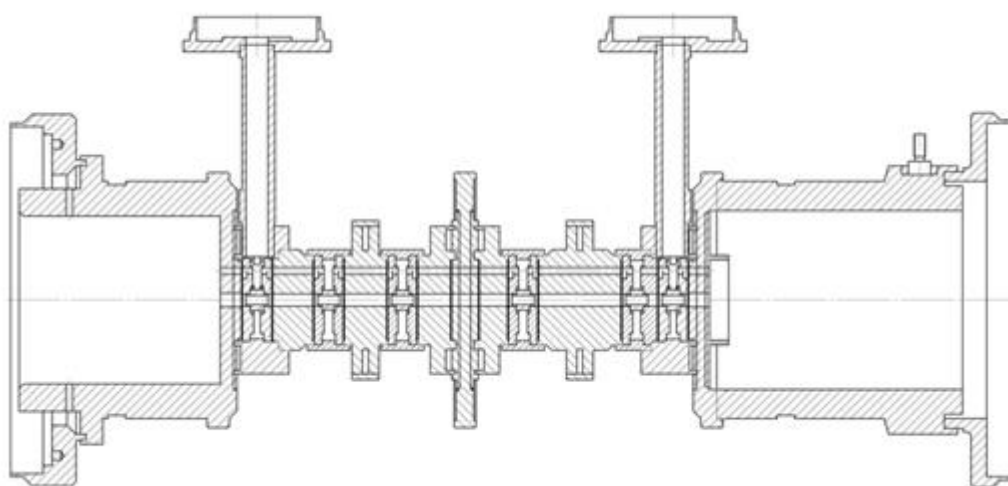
Эскиз резонаторного блока клистрона КИУ-283
